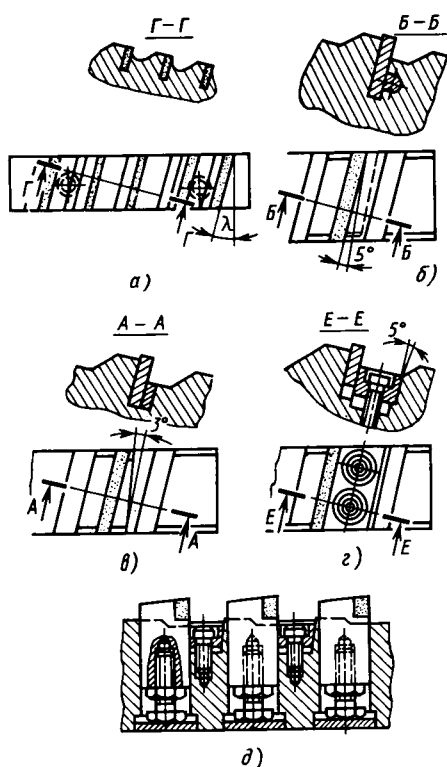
Крепление твердосплавных пластин и вставок в сечениях наружных протяжек
